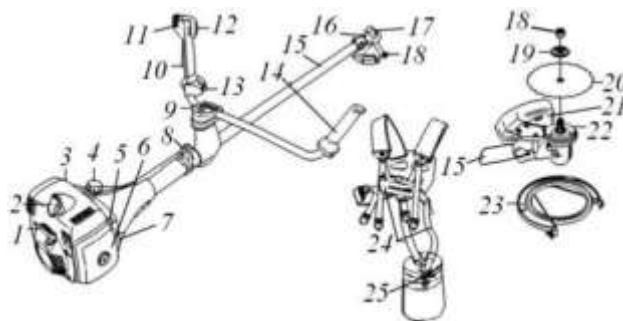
Мотокусторез «Husqvarna»: 1 - стартер; 2 - свеча зажигания; 3 - крышка; 4 - топливный бак; 5 - рычаг подсоса; 6 - карбюратор; 7 - крышка воздушного фильтра; 8 - подвеска ремней лямки; 9 - винт рукоятки; 10 - кнопка блокировки подачи топлива; 11 - выключатель двигателя; 12 - рычаг подачи топлива; 13 - подогрев рукояток; 14 - ручка левой руки; 15 - штанга; 16 - редуктор; 17 - пробка; 18 - гайка; 19 - нажимной диск; 20 - зубчатый пильный диск; 21 - защитный кожух; 22 - поводковый патрон; 23 - защита рабочего органа при транспортировании; 24 - лямка; 25 - карабин
